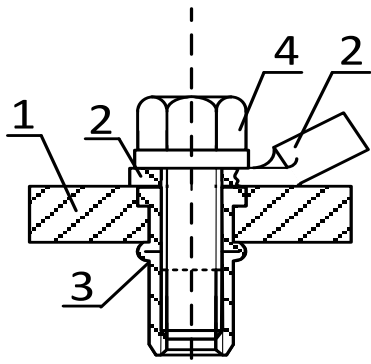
Контактное соединение шин ШУП-МСУ через гайку-заклёпку (1 - медная шина; 2 – кабельный наконечник; 3 – болт с зубчатым фланцем; 4 – контактная гайка-заклепка).
